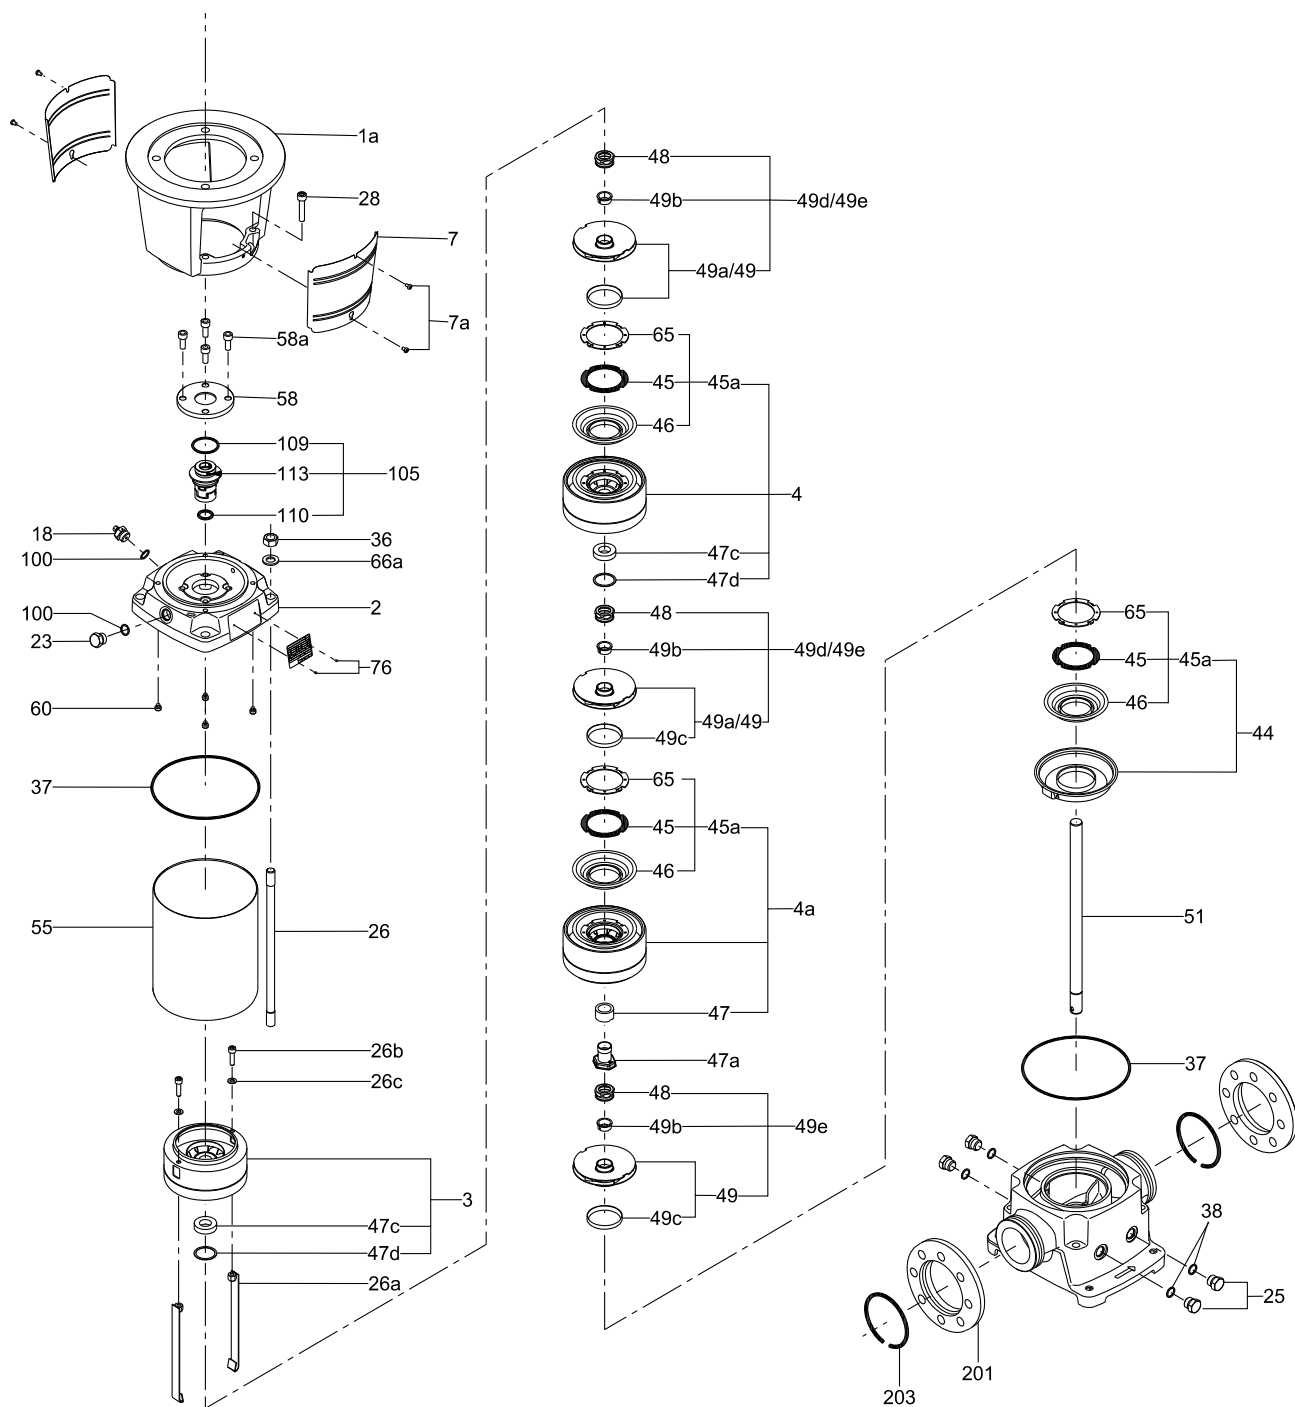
分解組立図 (詳細) CR, CRI, CRN 32 Model B
